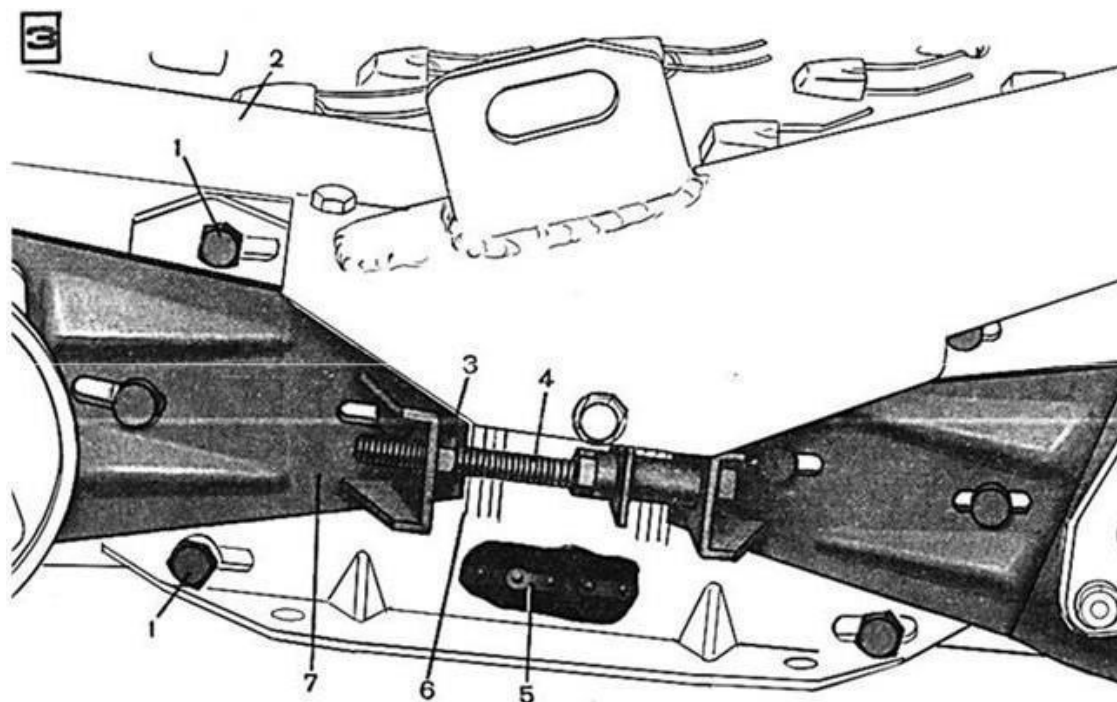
Схема регулировки натяжения тяговых цепей транспортёра:
